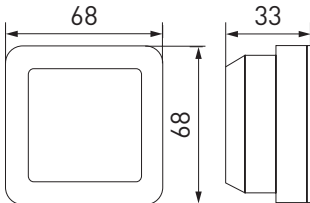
Габаритные размеры 1-клавишного выключателя
